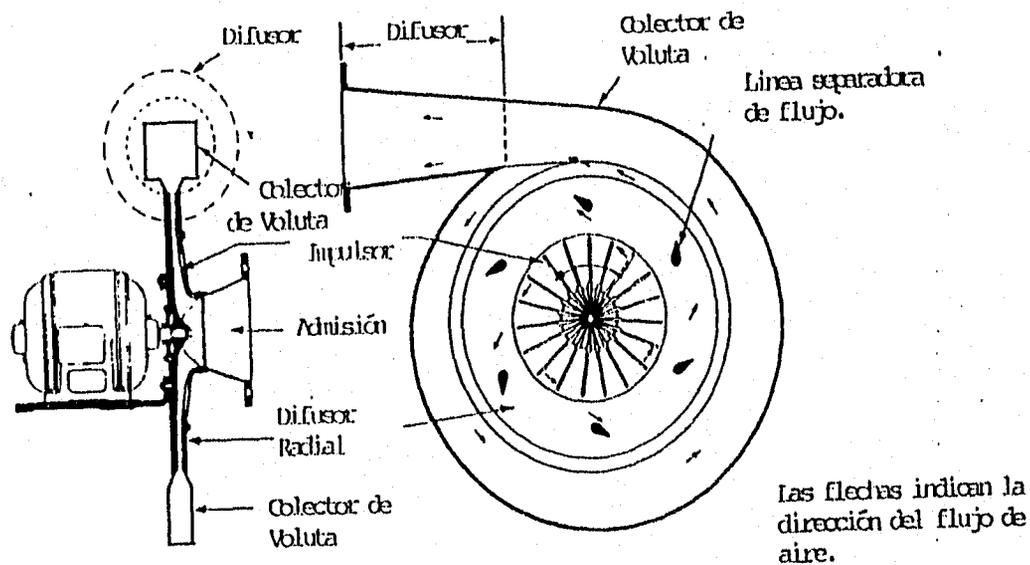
COMPRESOR CENTRIFUGO DE UNA SOLA ETAPA
